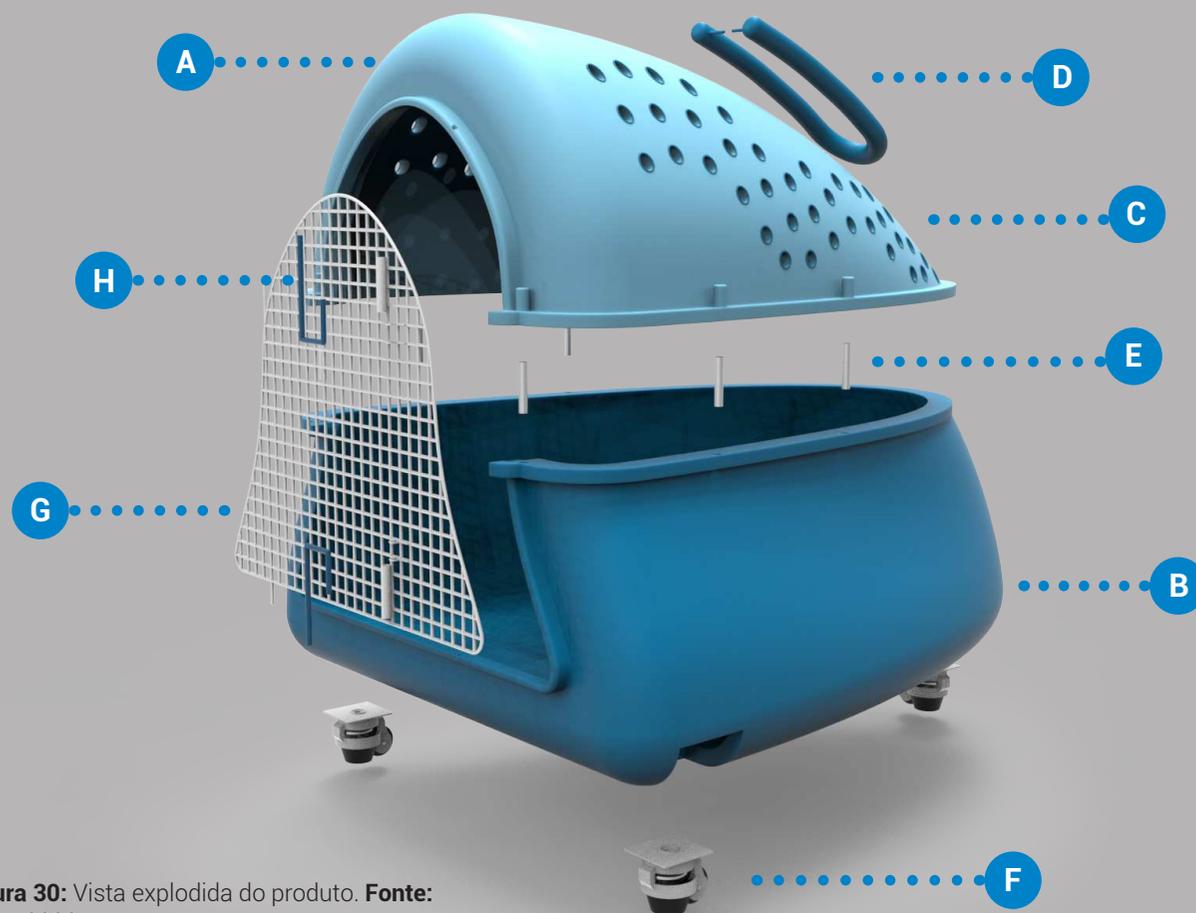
Vista explodida do produto. Fonte: Autor, 2022.
